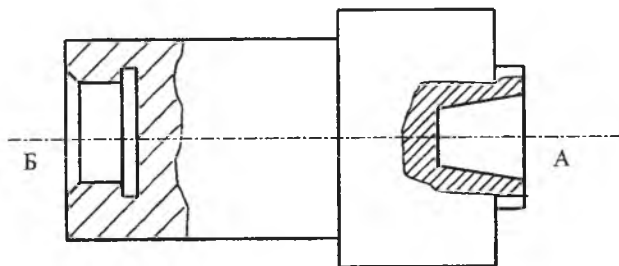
Виды углублений в заготовке для обеспечения жесткости врезания кольцевой головки
